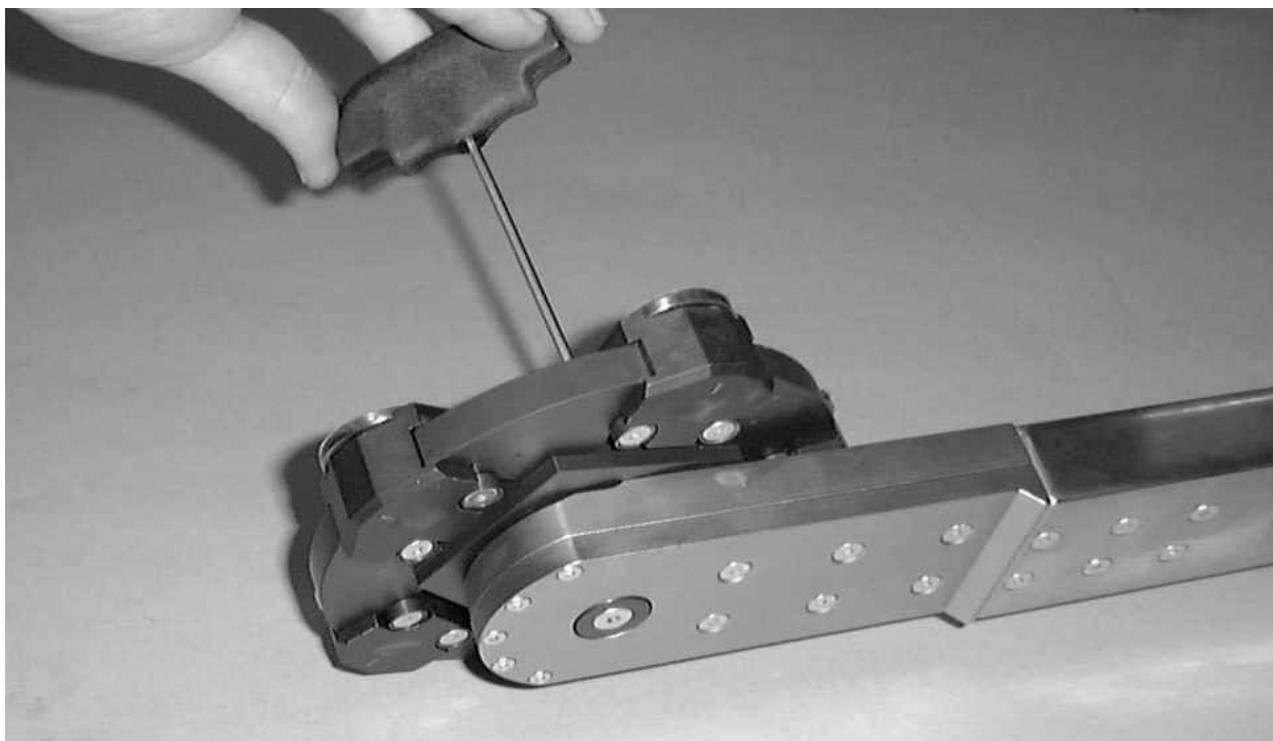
Установка планетарного колеса диаметром 100 или 135 мм
